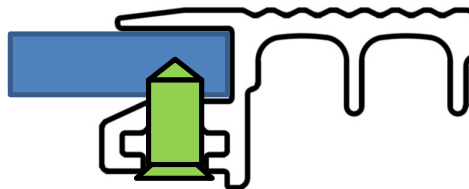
Bohrschraube ST3.5 x 13 oder Gewindefurchende Schraube M4x10 eindrehen
